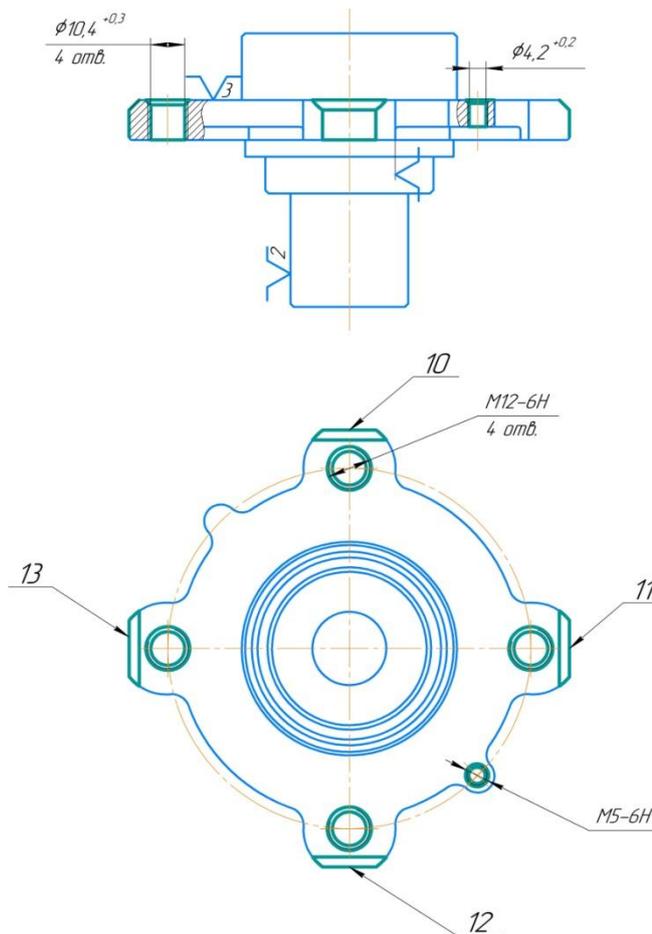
Эскиз для фрезерной операции с ЧПУ 020
